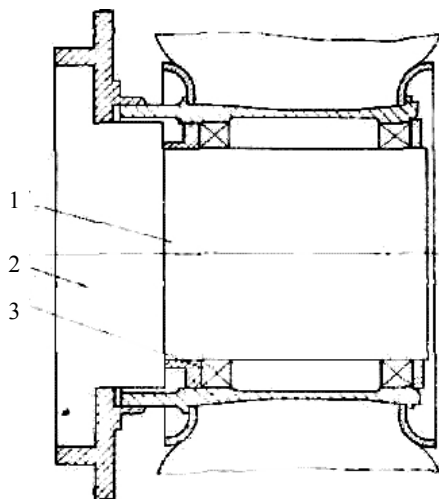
Схема мотор-колеса при компоновке V вида
